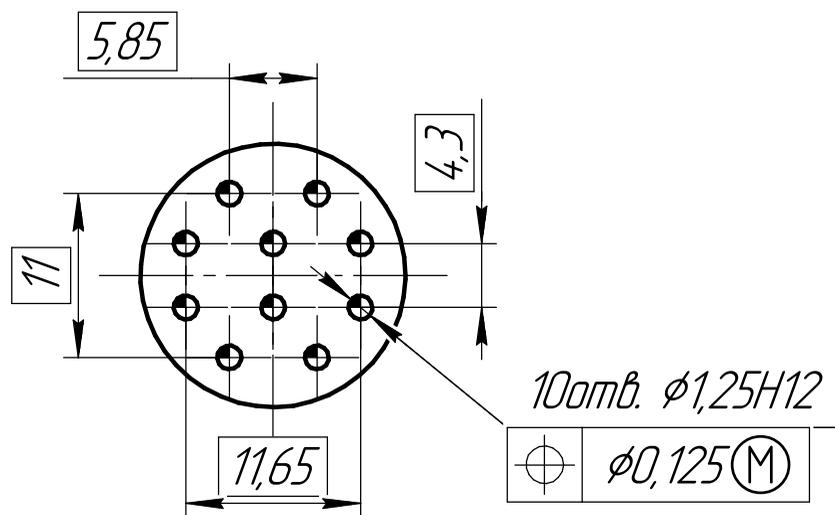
Разметка отверстий для ОСН-25-10/22...П-...
